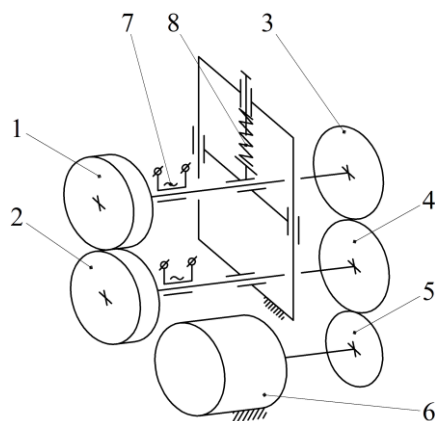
Кинематическая схема устройства проходного типа для обработки обувной резинки
